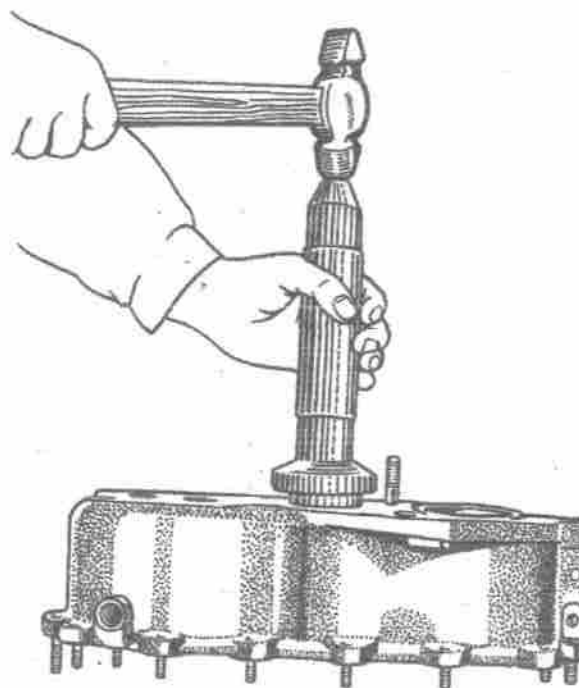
Einbauen des Rollenlagers ins Getriebegehäuse
